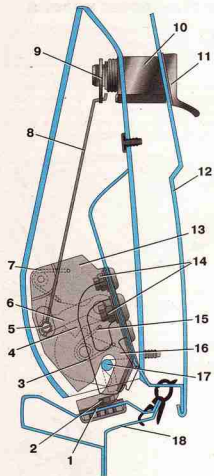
Замок крышки багажника: 1 – пластина фиксатора; 2 – болт крепления фиксатора замка; 3 – пружина ротора; 4 – собачка замка; 5 – винт крепления тяги привода; 6 – рычаг; 7 – пружина собачки замка; 8 – тяга привода; 9 – поводок привода; 10 – крышка багажника; 11 – ручка привода замка; 12 – крышка багажника; 13 – замок крышки багажника; 14 – гайки крепления замка; 15 – пружина ротора; 16 – ротор замка; 17 – фиксатор замка; 18 – верхняя поперечина задка кузова
